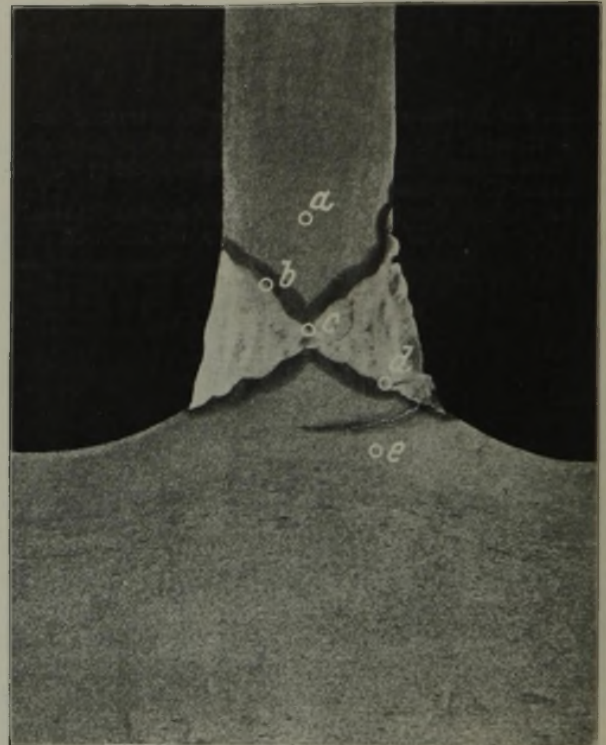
Schnitt durch die Schweißnaht nahe dem Querriß, geätzt, mit einem Längsriß.
